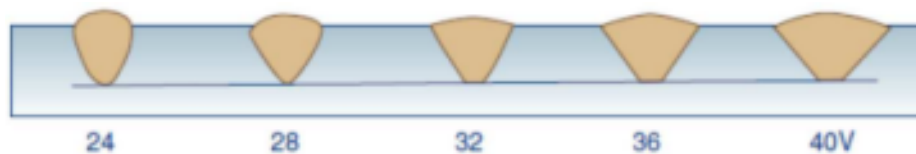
Вплив зміни напруги на форму зварювального шва
